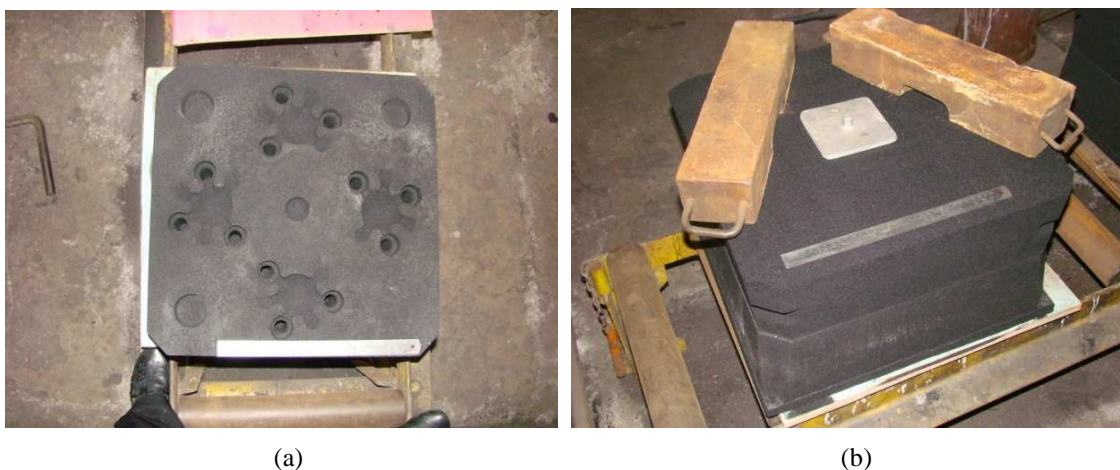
(a) Molde aberto mostrando as cavidades dos pinos e (b) molde fechado com a parte superior do molde.
